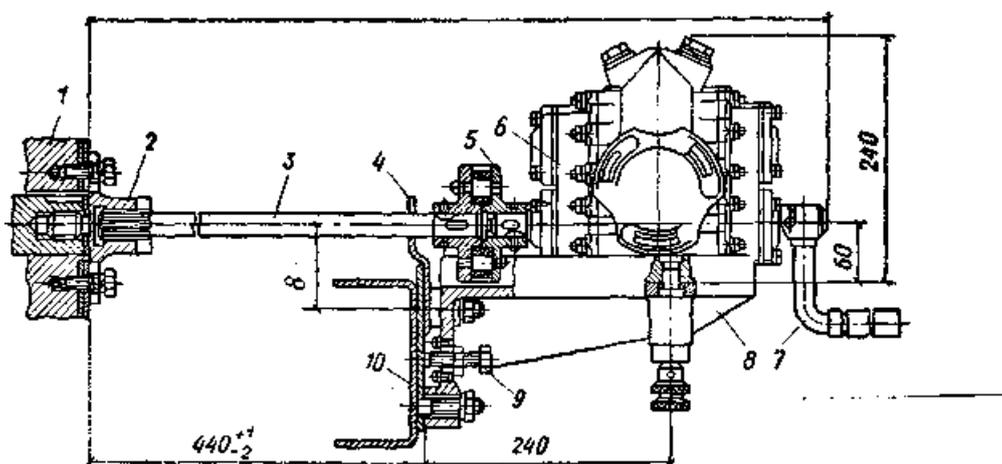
Установка насоса НШН–600 на шасси автомобилей ГАЗ: 1 – шкив коленчатого вала двигателя; 2 – храповик; 3 – вал привода; 4 – кронштейн заводной рукоятки; 5 – муфта в сборе; 6 – насос; 7 – заводная рукоятка; 8 – кронштейн в сборе; 9 – регулировочный болт; 10 – косынка в сборе
